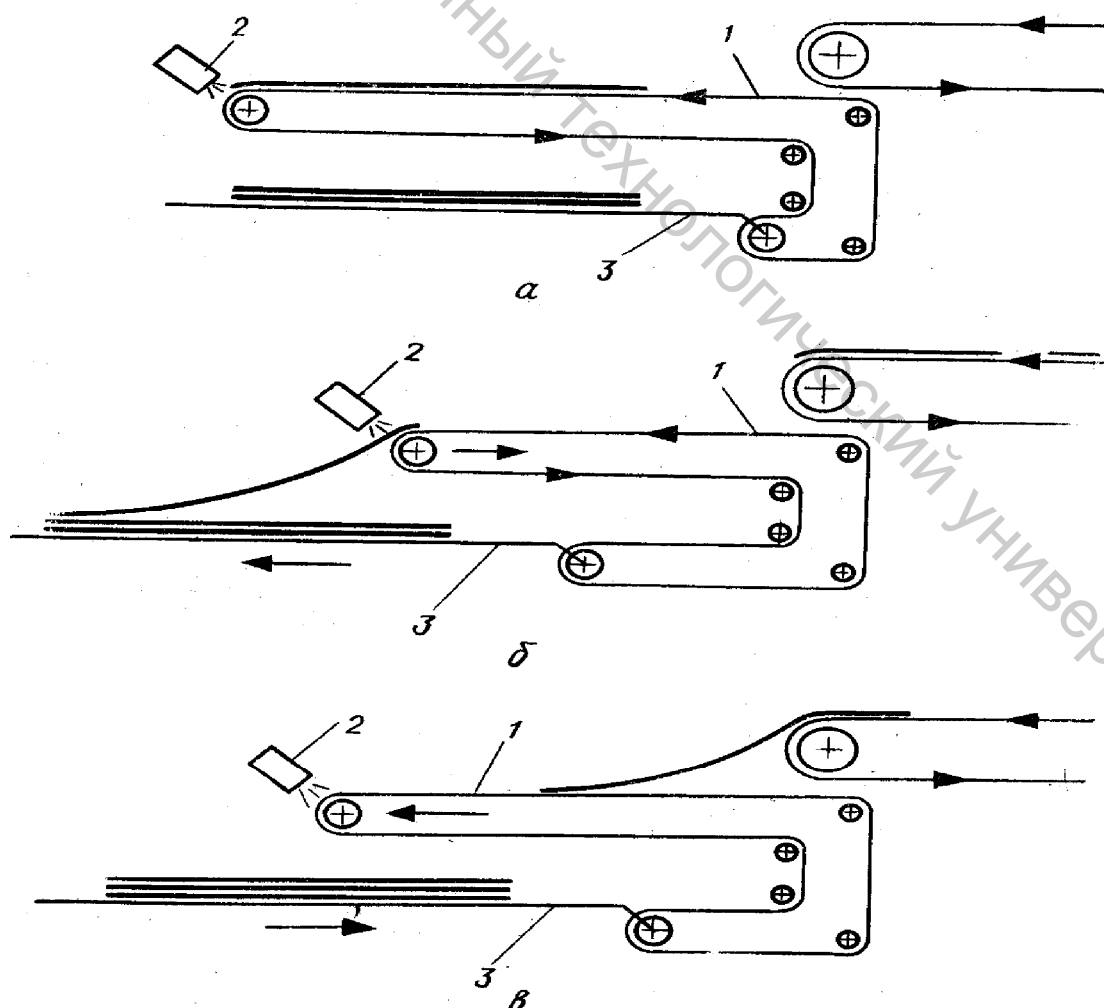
Схема конструкции укладчика деталей к прессам и принцип
